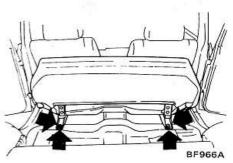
Dépose du coussin de siège arrière (Commerciale et Fourgonnette)
